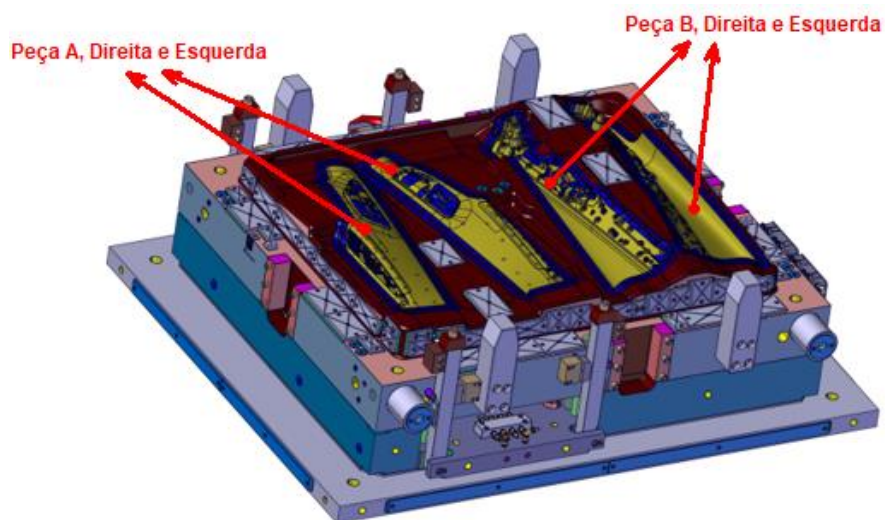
Exemplo de um molde família fabricado na SF Moldes.
